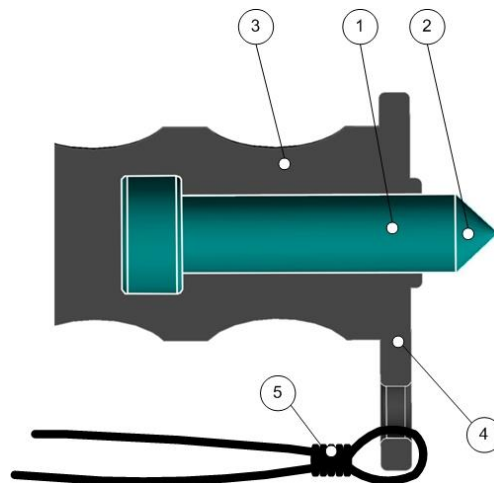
Стеклобой ударного типа (в разрезе): 1- металлический боек; 2 – концентратор напряжений; 3 – рукоять; 4 – гарда; 5- темляк
